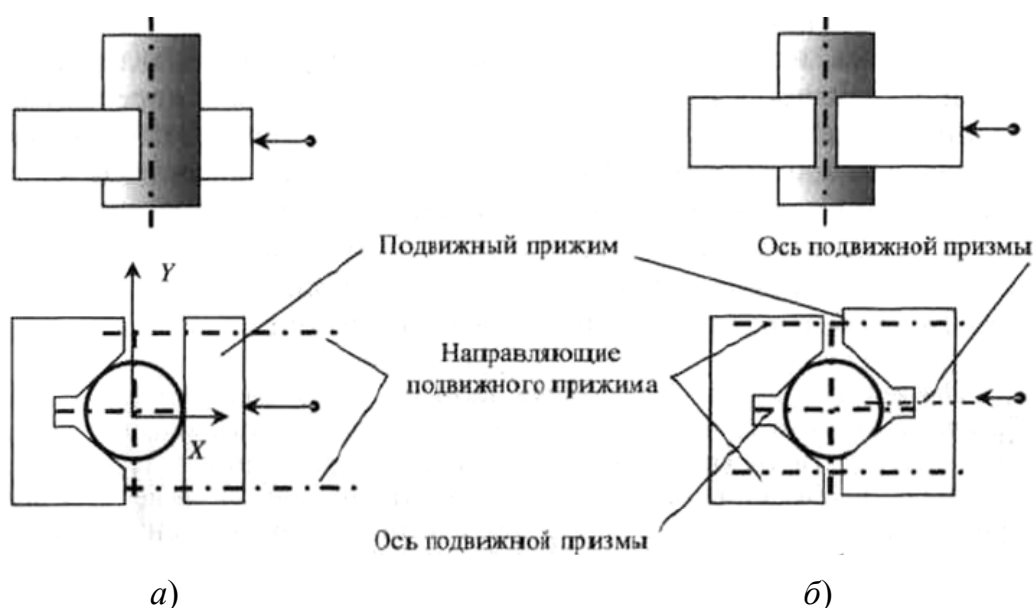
Схема базирования цилиндрической заготовки:
